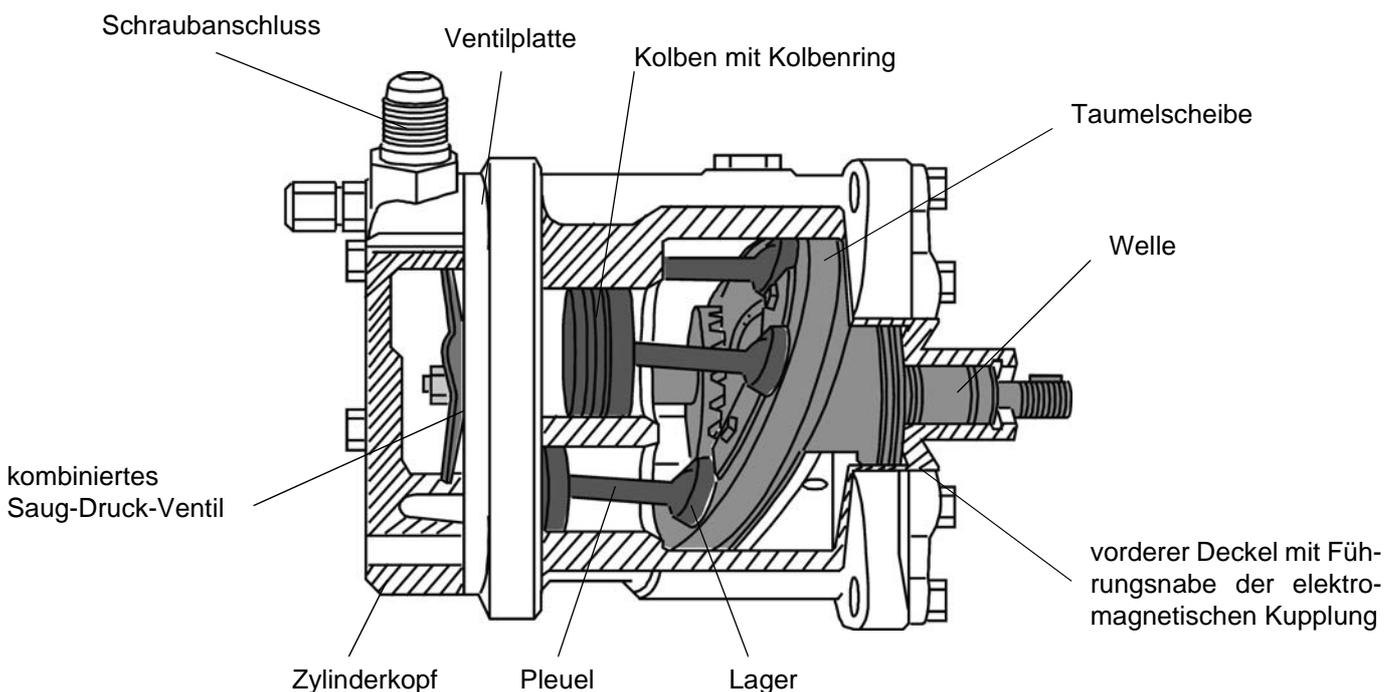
Schnitt durch einen Axialkolbenverdichter
